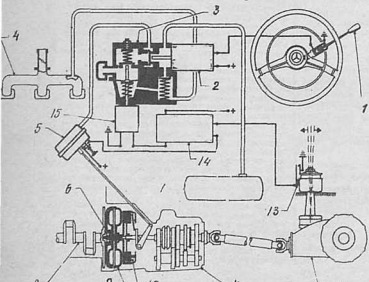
Схема электровоздушного автомата сцепления «Гидракс»: 1 — рычаг переключения передач и электроконтакт; 2 — магнит; 3 — клапан управления сервоагрегата; 4 — впускной коллектор двигателя; 5 — сервомотор; 6 — свободный ход; 7 — вакуумный резервуар; 8 — коленчатый вал двигателя; 9 — гидромумфта; 10 — механическое сцепление; 11 — коробка передач; 12 — задний мост; 13 — датчик заднего моста; 14 — реле; 15 — магнит.
